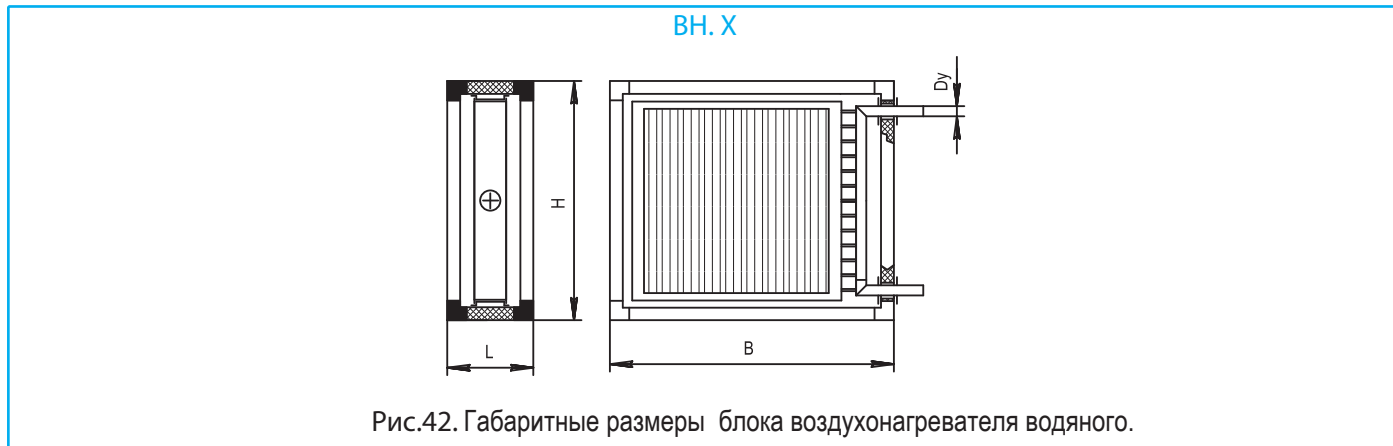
Габаритные размеры блока воздушонагревателя водяного.
